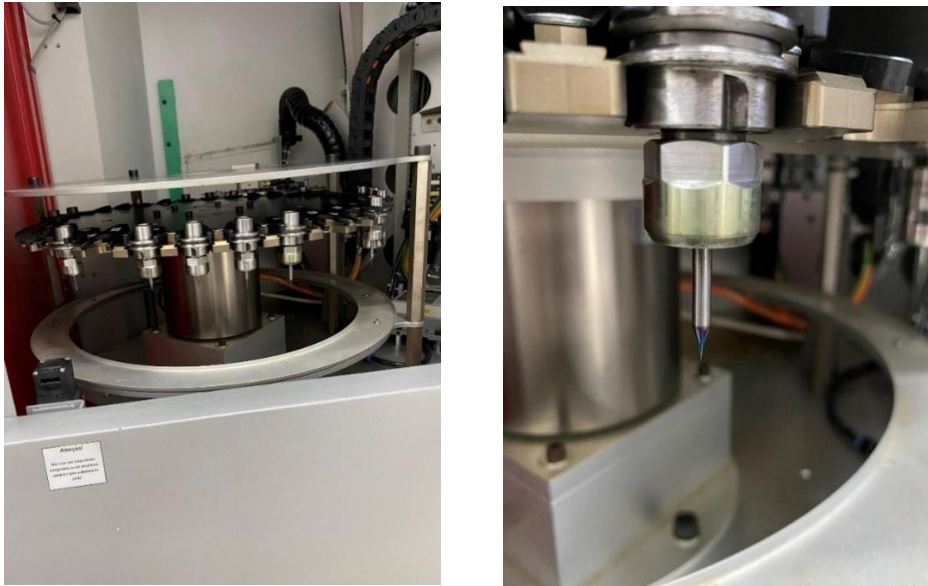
Conjunto de “brocas” para a usinagem de precisão
